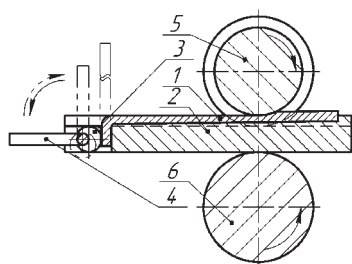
Схема прокатки полосы с рассогласованием окружных скоростей деформирующего инструмента и фиксацией конечного участка: 1 – заготовка; 2 – калибрующая оправка; 3 – кулачковый зажим; 4 – рычаг; 5 – верхний валок; 6 – нижний валок
